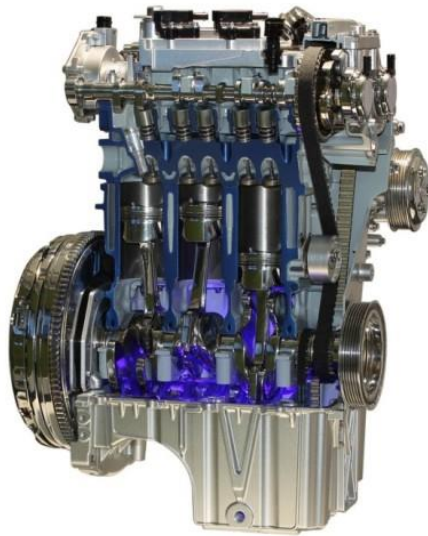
Motor tricilindrico Ecoboost de Ford. [21]
